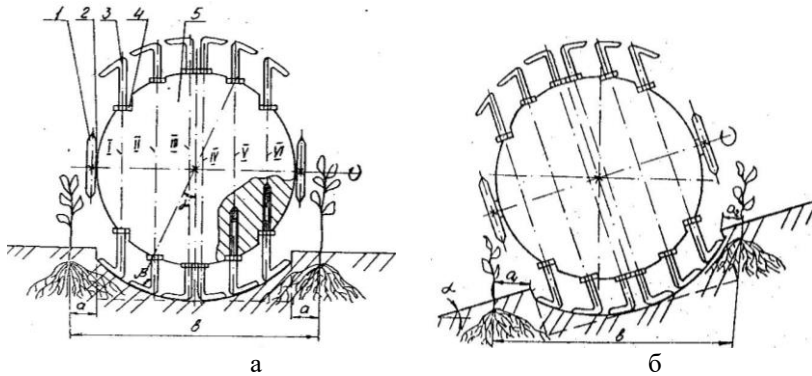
Сферична фреза для обробітку ґрунту: а – при роботі на рівнині; б – при роботі на схилі; 1 – зірочки; 2 – вал; 3 – ґрунтові ножі; 4 – контргайки; 5 – кульова поверхня
